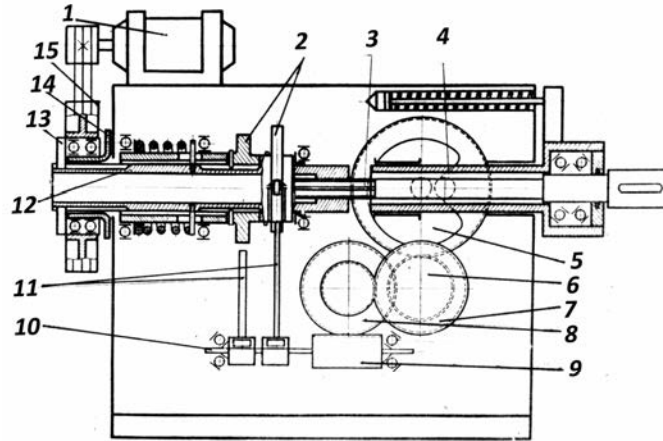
Передаточний механізм силової головки агрегатного верстата
